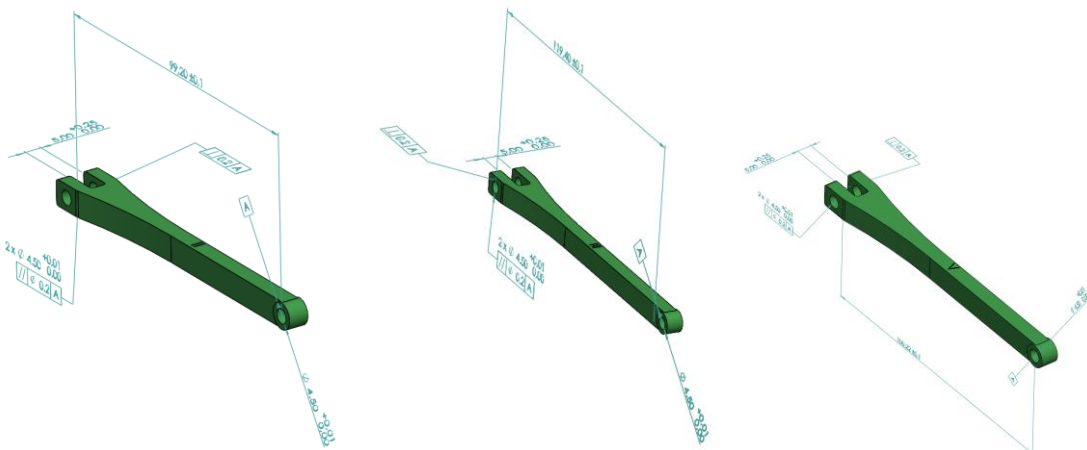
Tolerancias dimensionales "Barra 3" dedos
